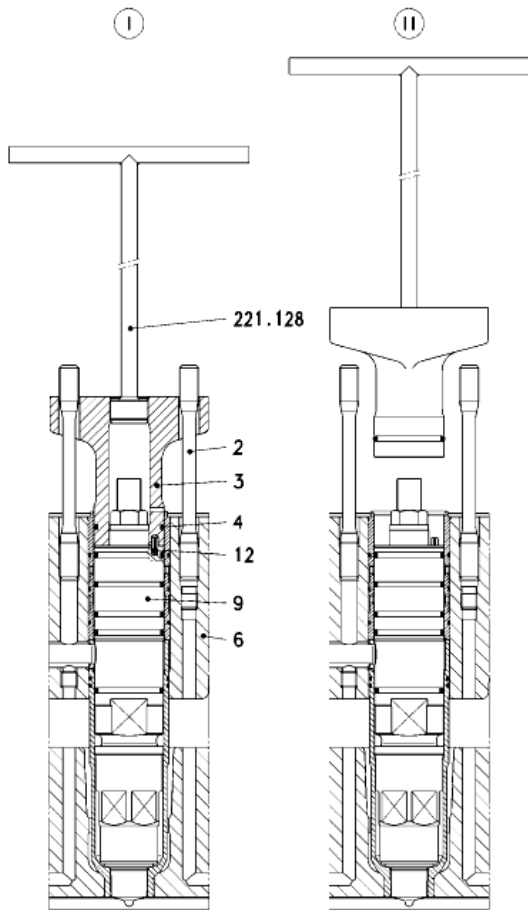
Зняття / встановлення тяги фланця: 2 – шпилька; 3 - упорний фланець; 4 - О-подібне кільце ущільнення; 6 - головка циліндра; 9 – паливна форсунка; 12 – штифт; I-II - робочі кроки
